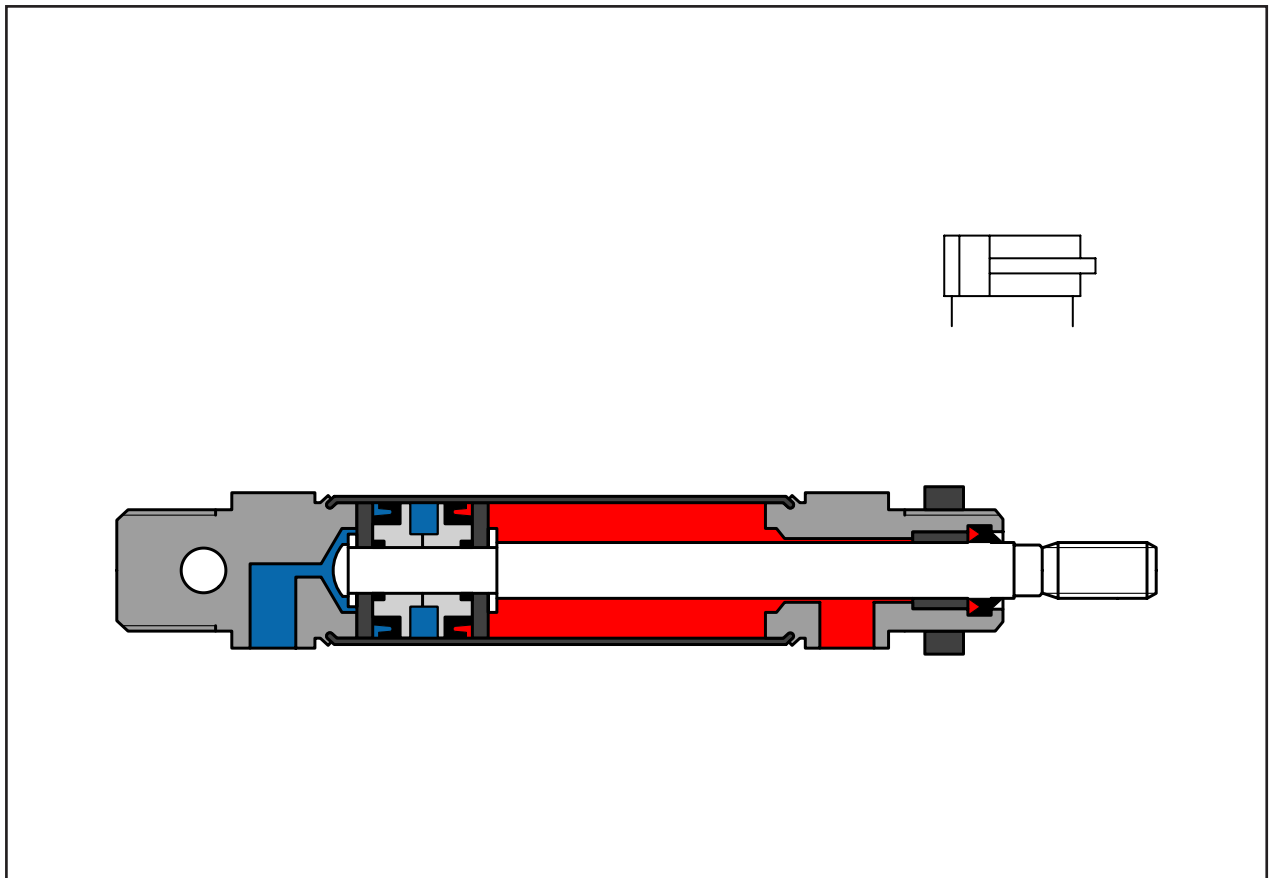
Doppeltwirkender Zylinder (Bild: BoschRexroth)
